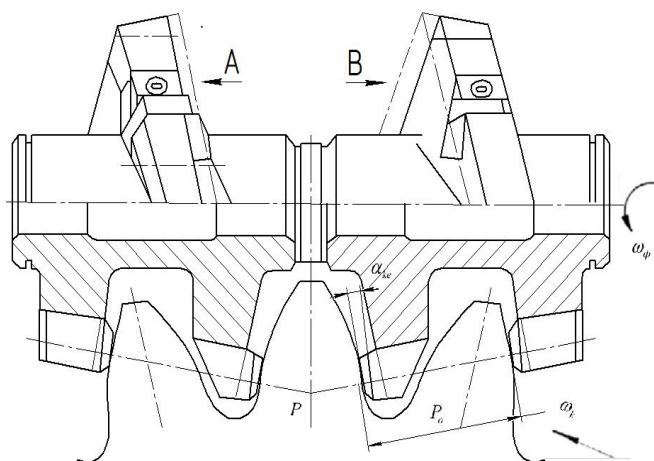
Принципова конструкція фрези з роздільною схемою формоутворення
